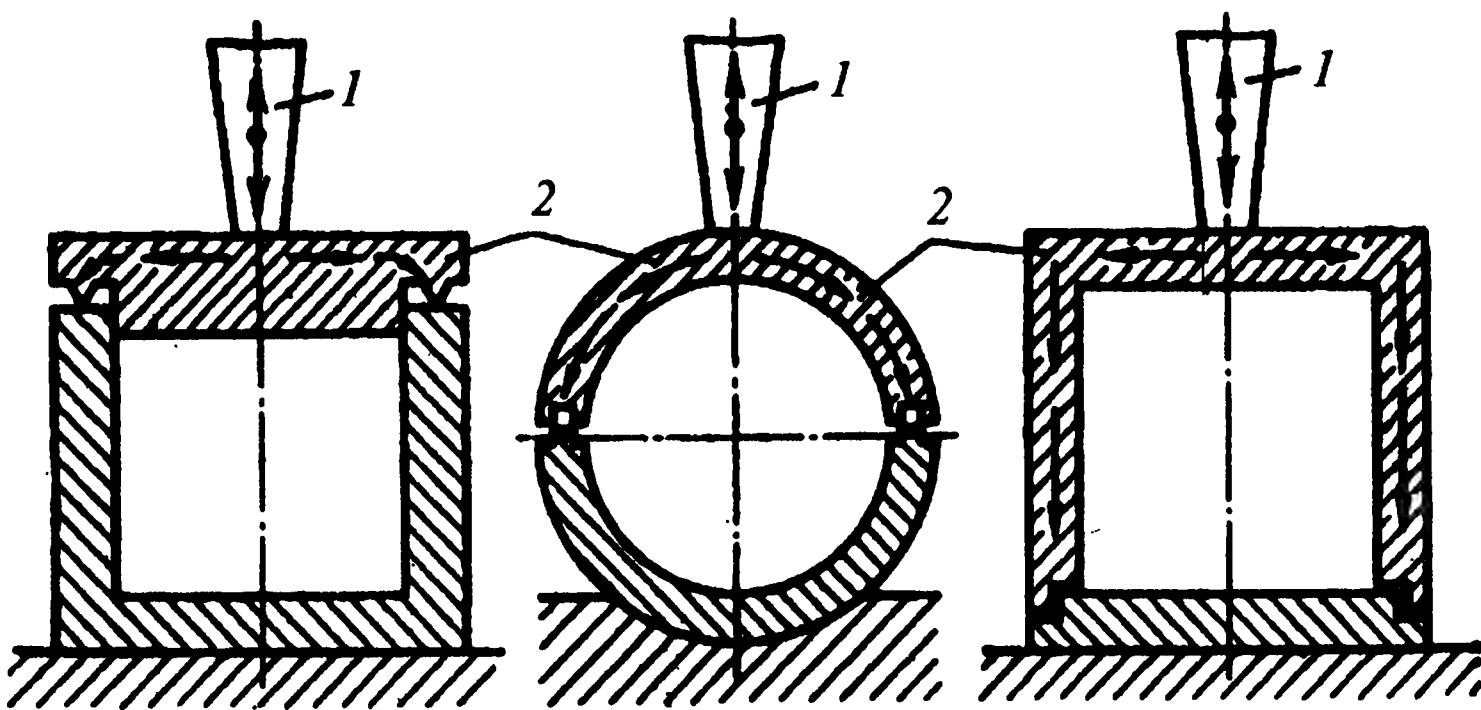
Схема передаточной ультразвуковой сварки:
